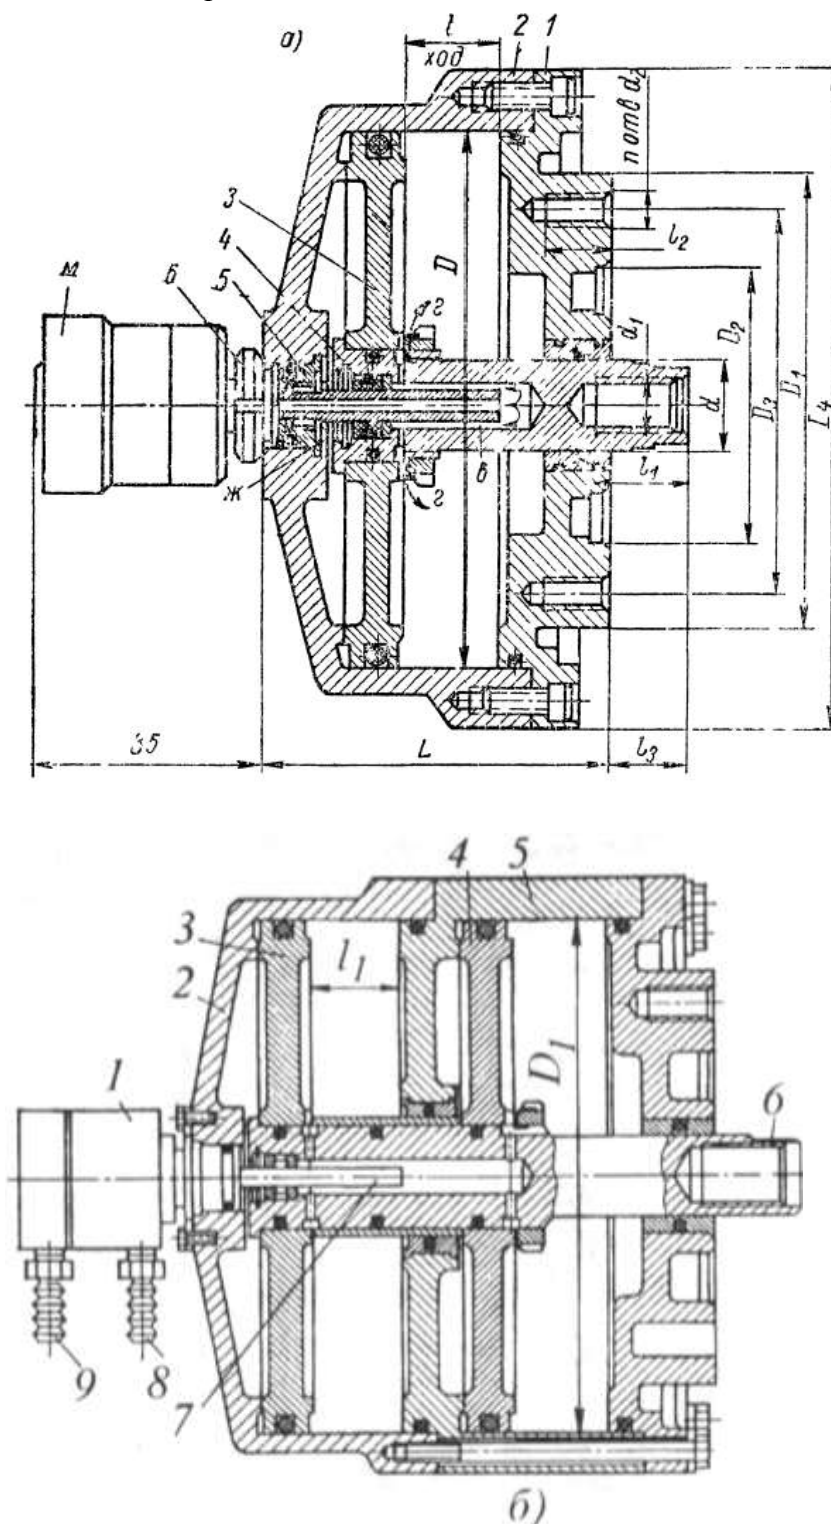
а) Конструкция цилиндра пневматического вращающегося *одинарного
